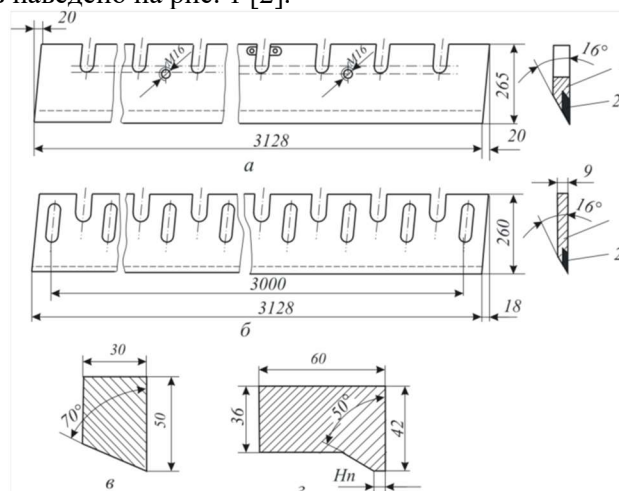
Конструкції ножів і притискних лінійок шпоностругальних верстатів: а – ніж до чеського верстата ФММ-3100 товстий; б – те ж тонкий; в, г – поперечні перерізи притискних лінійок до шпоностругальних верстатів: 1 – корпус ножа; 2 – робоча (різальна) частина
